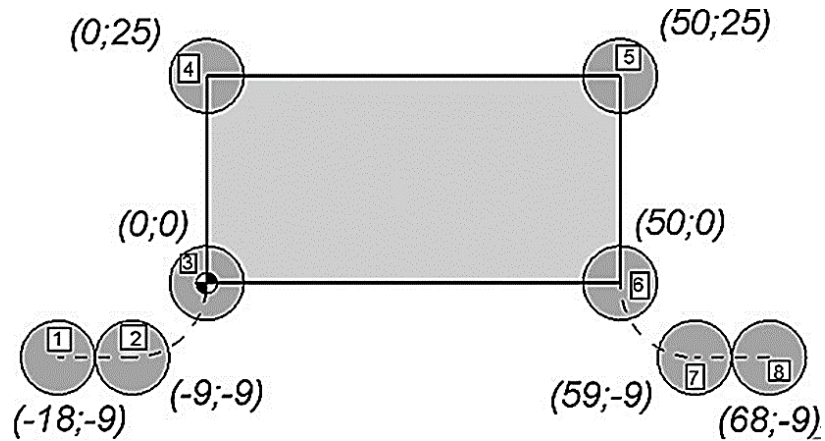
Оброблюваний контур для фрези Ø9 мм.
